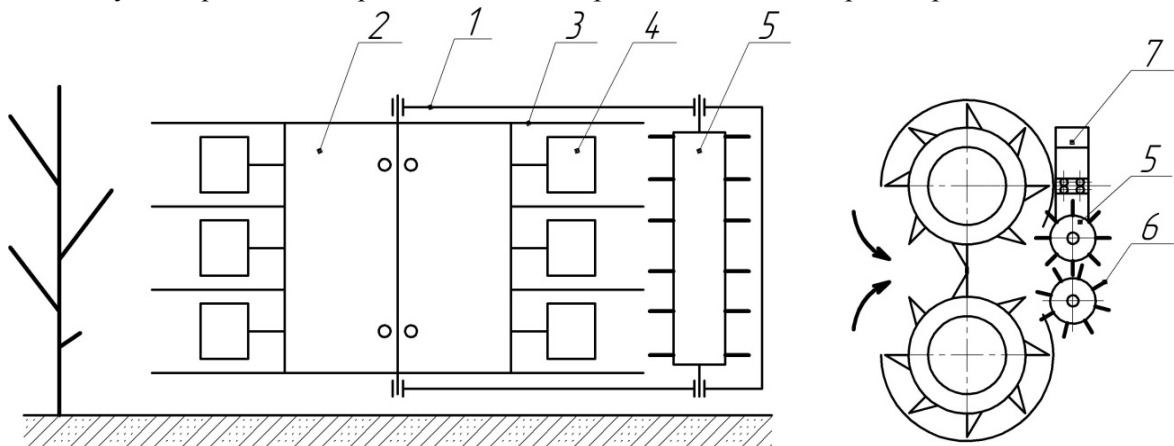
Схема роботи ножового апарату машини для подрібнення енергетичної верби: 1 – рама машини; 2 – ножовий барабан; 3 – дискові ножі; 4 – лопатки що подають продукцію; 5 – подрібнювач; 6 – ножі подрібнювача; 7 – вентилятор.
